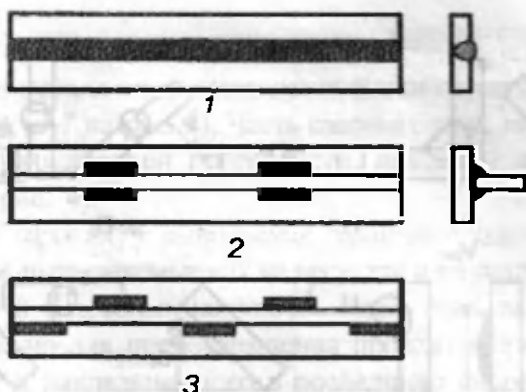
Классификация сварных швов по протяжённости: 1 – непрерывный; 2 – цепной; 3 – шахматный
